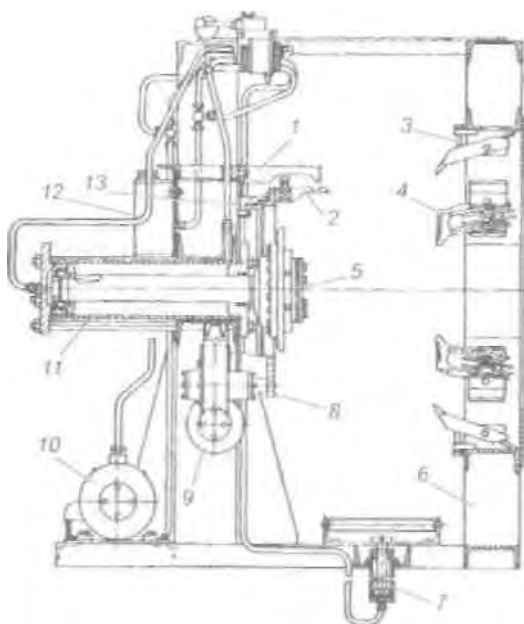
Стенд для демонтажа и монтажа шин грузовых автомобилей: / — упор; 2 — съемник замочного кольца; 3 — винт; 4 — лапа; 5 — пневматический патрон; 6 — рама; 7 — гидравлический подъемник; 8 — зубчатое колесо; 9 — редуктор; 10 — гидравлический привод; 11 — гидравлический цилиндр; 12 — бачок; 13 — обечайка
